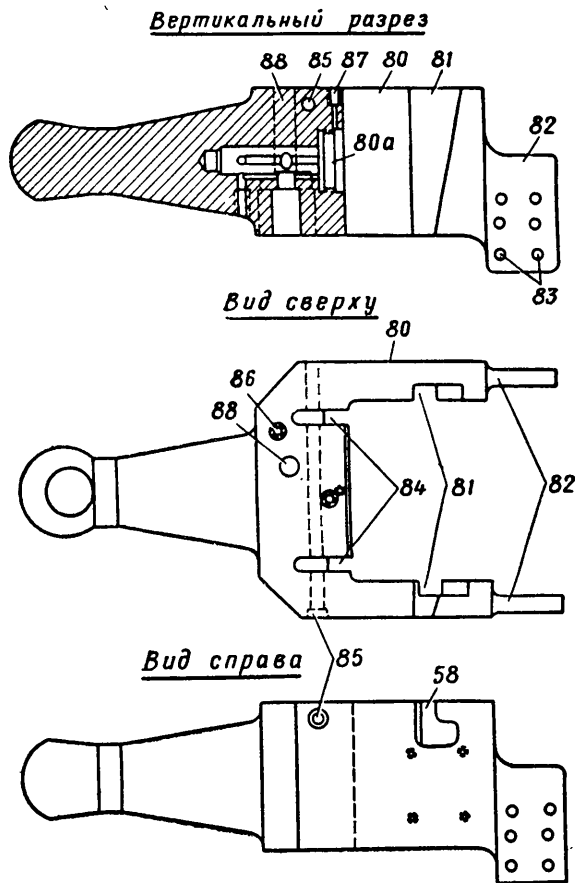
Корпус казенника (02-1) минометов старой конструкции:
